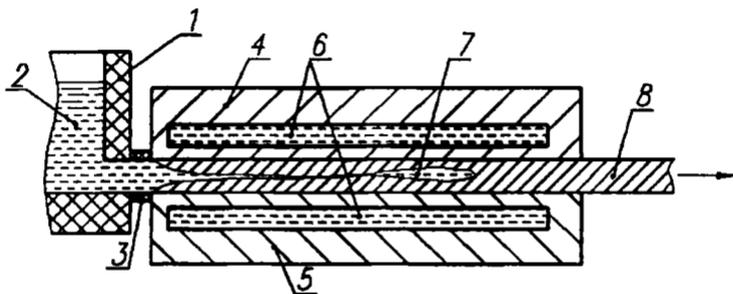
Схема формирования отливки при горизонтальном непрерывно-шаговом литье: 1 – металлоприемник; 2 – расплав; 3 – соединительный стакан; 4 – полуформа верхняя; 5 – полуформа нижняя; 6 – водяное охлаждение; 7 – незатвердевший металл; 8 – отливка
